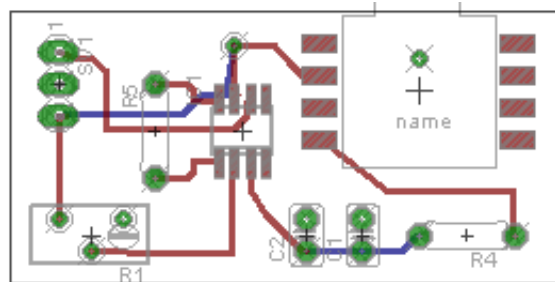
Placa de circuito impresso para condicionamento do sinal do sensor MPXV5004DP
